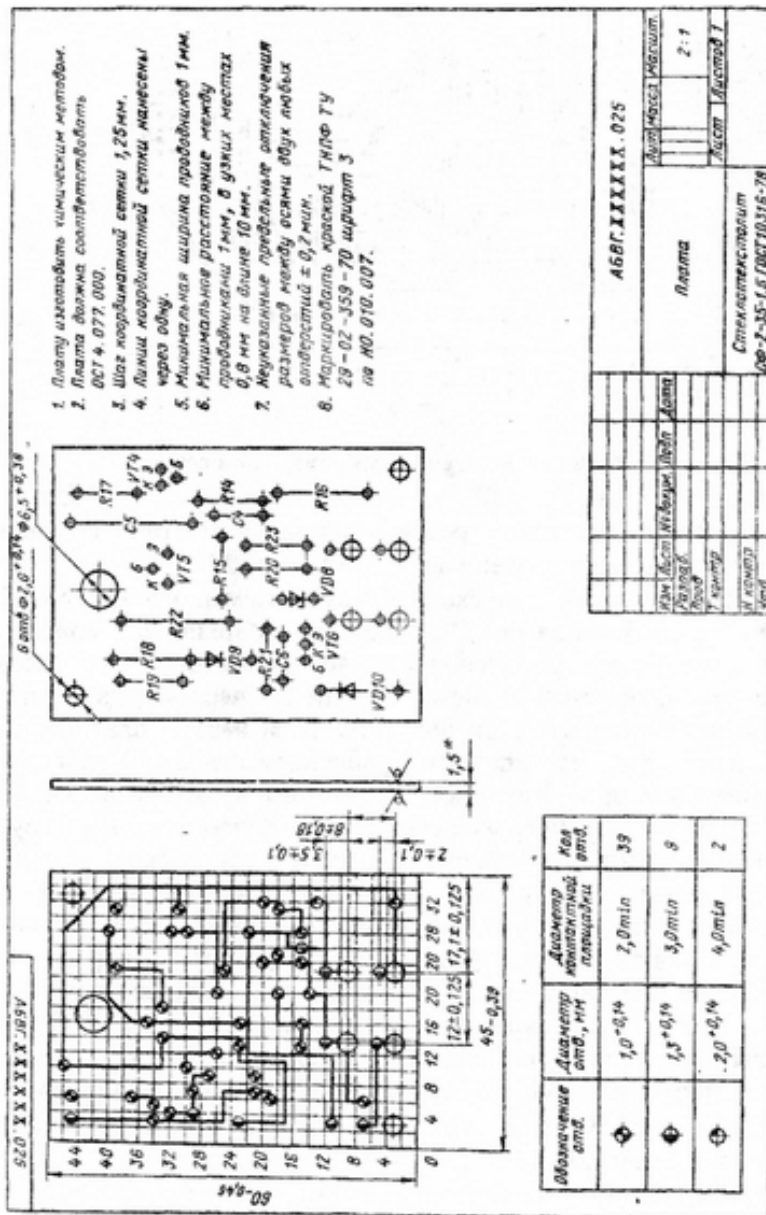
Чертеж печатной платы с комбинированным способом нанесения размеров
